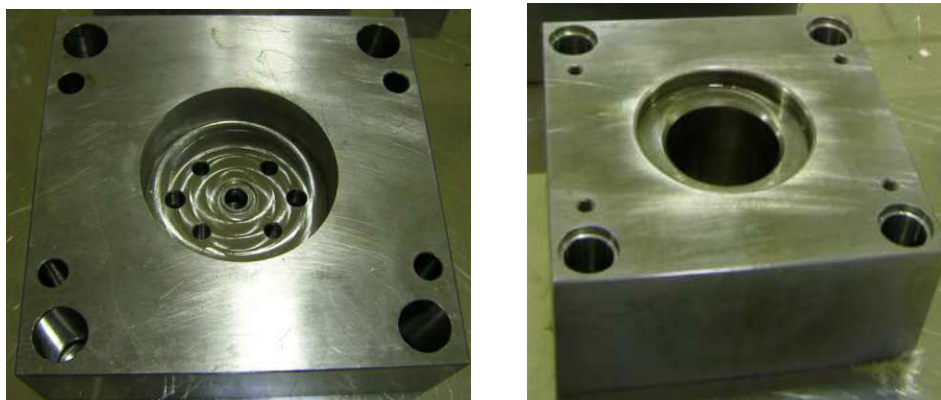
Chapa da bucha e chapa da cavidade do molde
